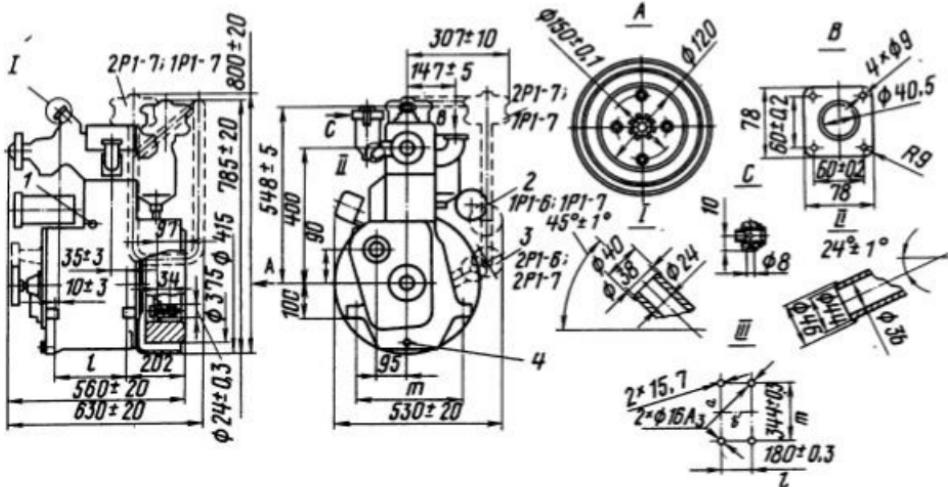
Габаритный чертеж дизеля 1Ч 8,5/11 (1Р1-6, 1Р1-7, 2Р1-6, 2Р1-7):
